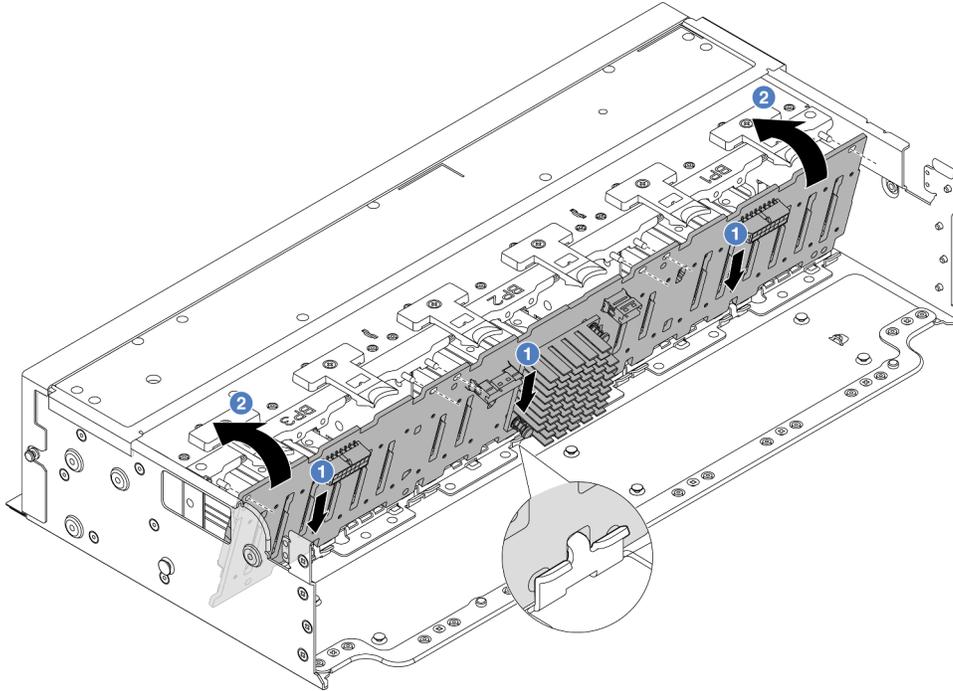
Installation du fond de panier d'unité 24 baies avec extension
